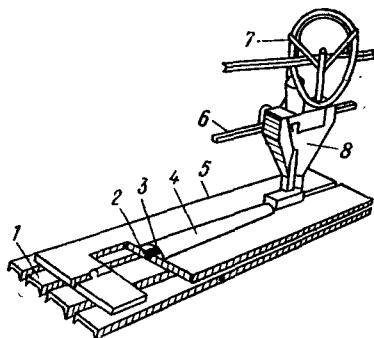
Схема автоматической сварки под флюсом (материал определенного химического состава)
